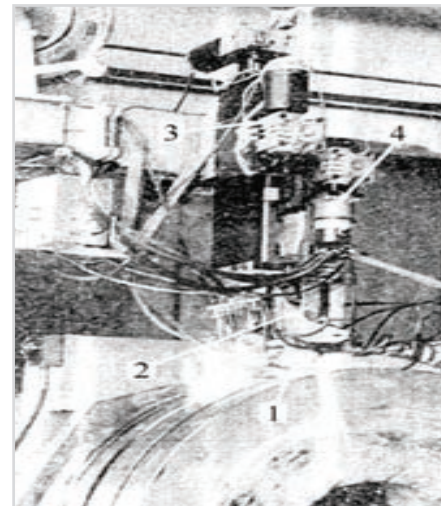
Автомат для сварки наружных кольцевых швов: 1 — защитное устройство; 2 — мундштук; 3 — суппорт; 4 — механизм подачи проволоки
